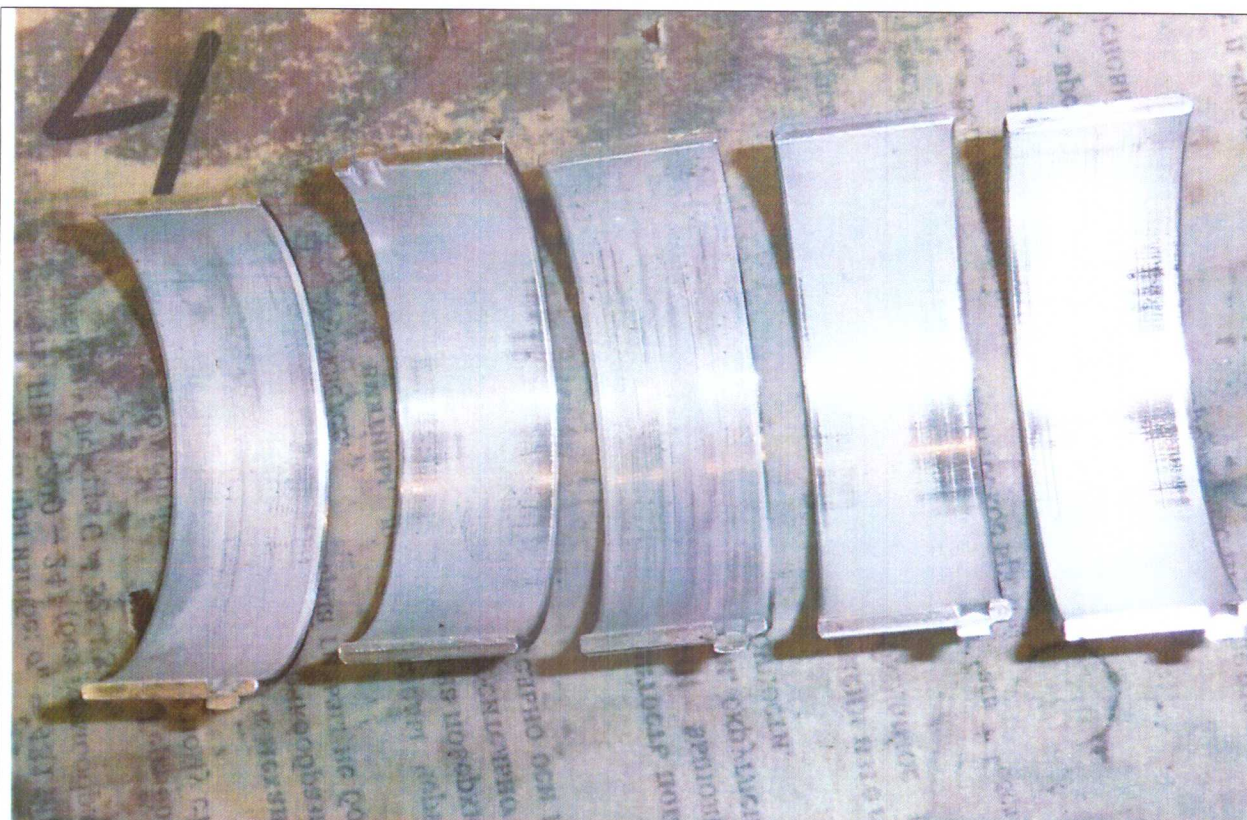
Внешний вид рабочей поверхности нижних вкладышей коренных подшипников коленчатого вала по окончании длительных испытаний двигателя при работе на базовом масле Castrol EDGE
